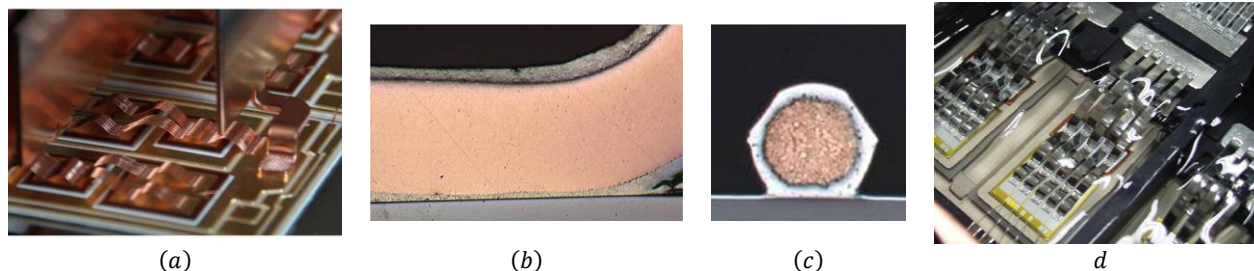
(a) : puces connectées par fils de bonding en cuivre [220]. (b-c) : vues en coupe d'un pied de fil de bonding Al/Cu de 300 µm de diamètre soudé sur une puce [223]. (d) : IGBT connecté par ruban aluminium [224].
